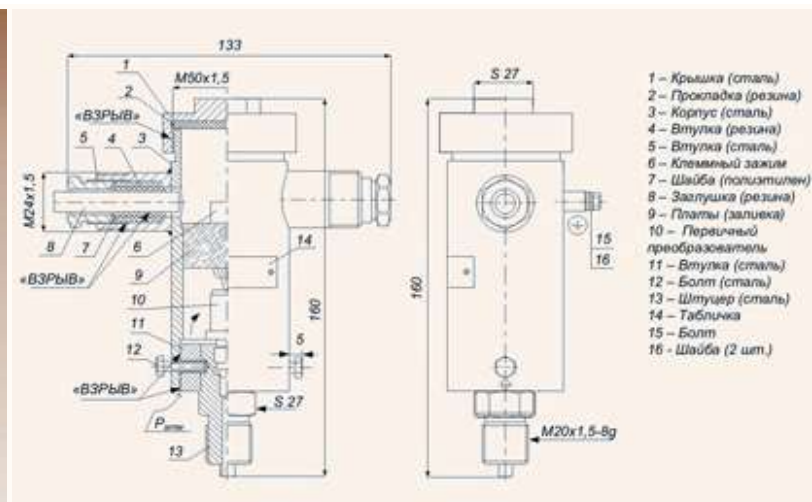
Датчик СЕНС ПД. Габаритный чертеж.
